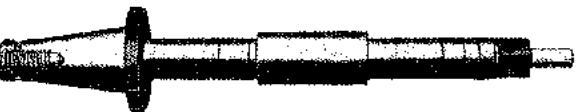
Barrena para fresa (Brown & Sharpe Mfg. Co.).
